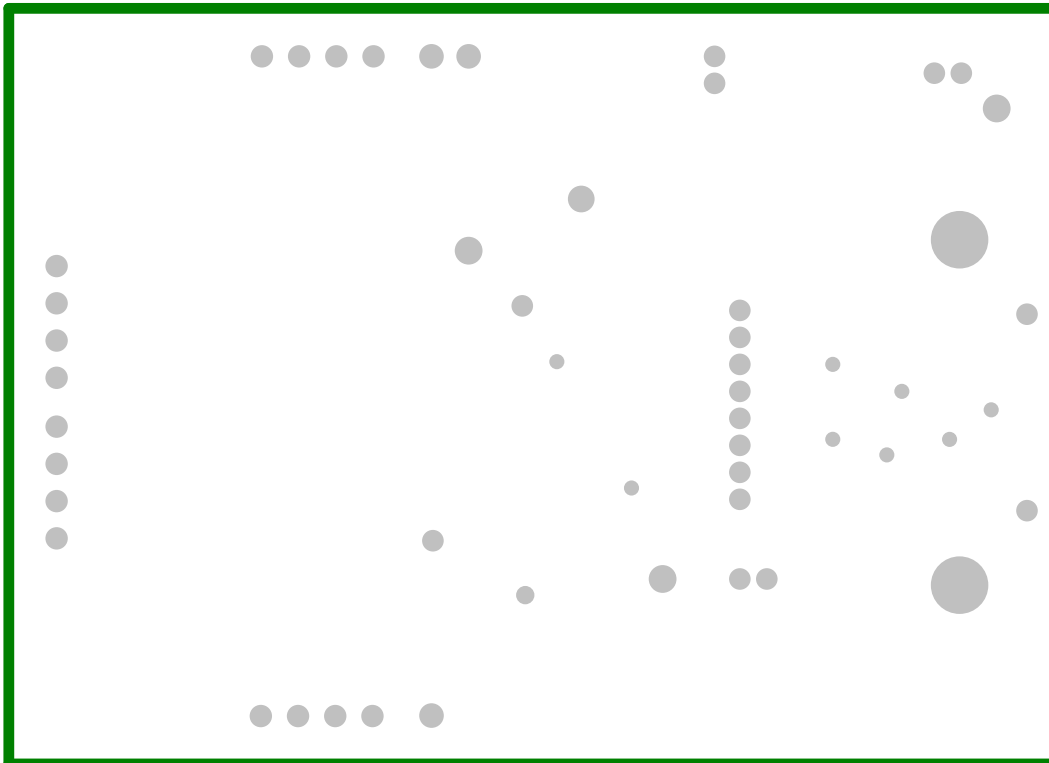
ADS125P08 EVM PCB 布局 — 接地层 (第 1 层)
